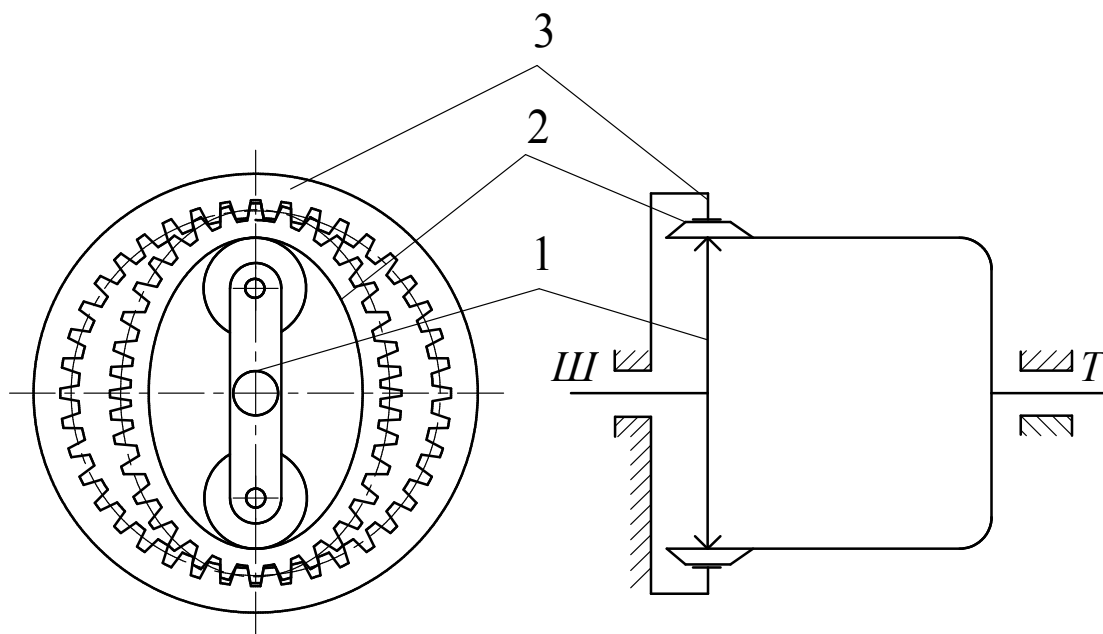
Кинематическая схема волнового редуктора: 1 - водило с двумя роликами; 2 - гибкое колесо; 3 - неподвижное колесо с внутренними зубьями.
